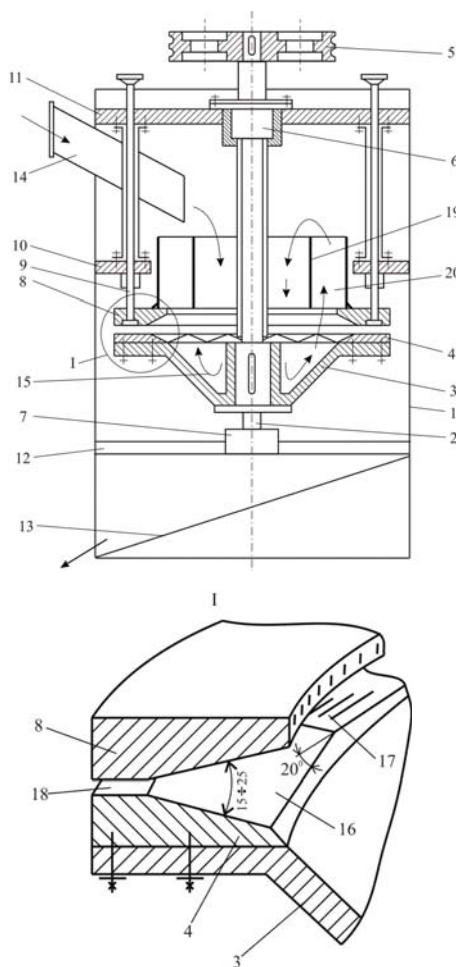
Дробильно-измельчительная установка (ДИУ)
